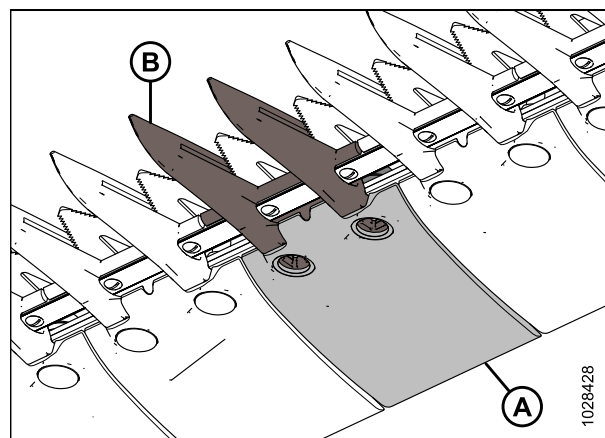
Заостренный противорежущий палец и износная пластина
